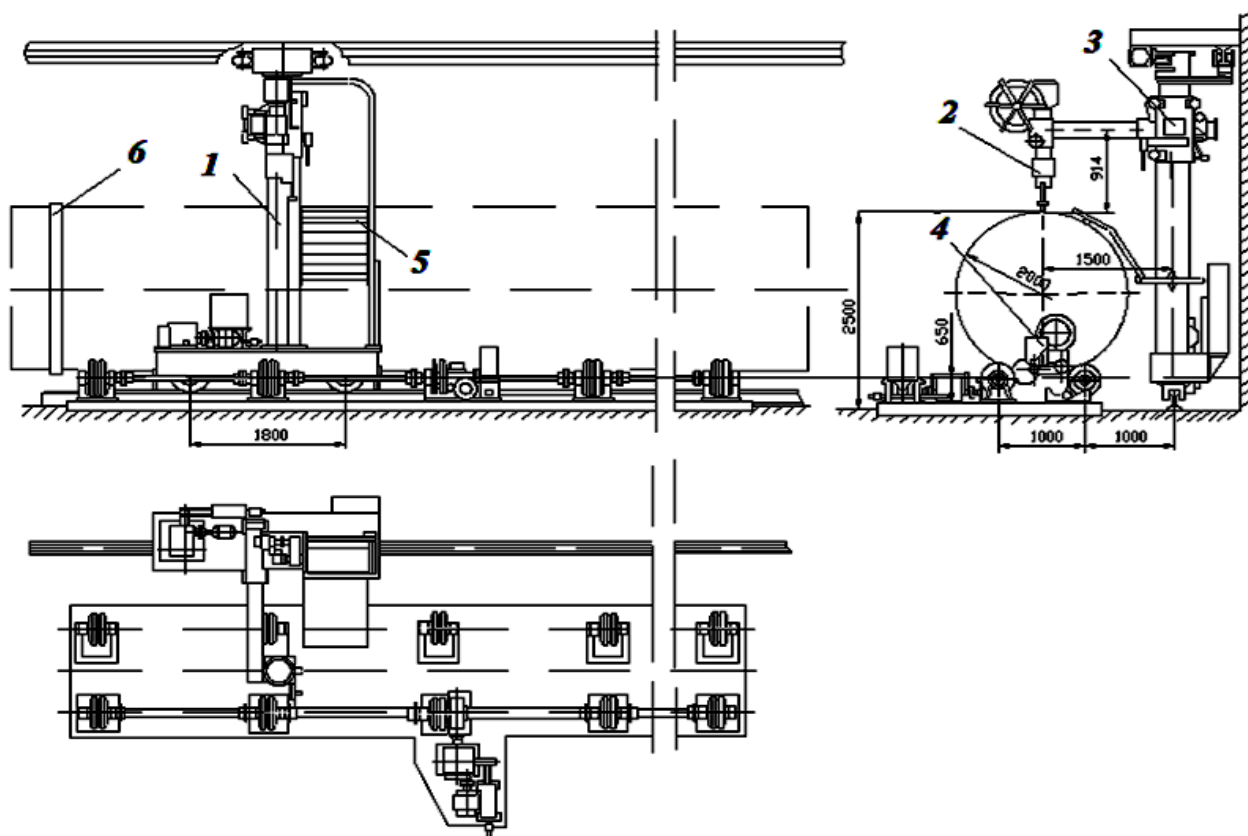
Установка для зварювання котлів цистерн із візком велосипедного типу:
